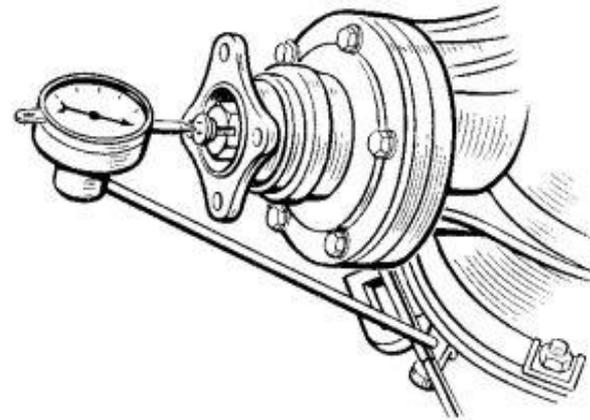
Определение осевого люфта в подшипниках ведущей шестерни главной передачи
